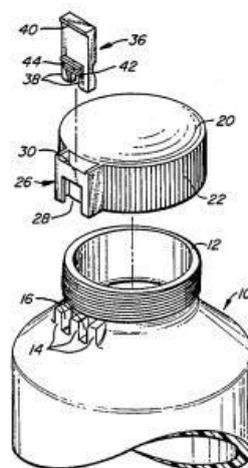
Locking screw cap (Tampa de travamento com pino)
